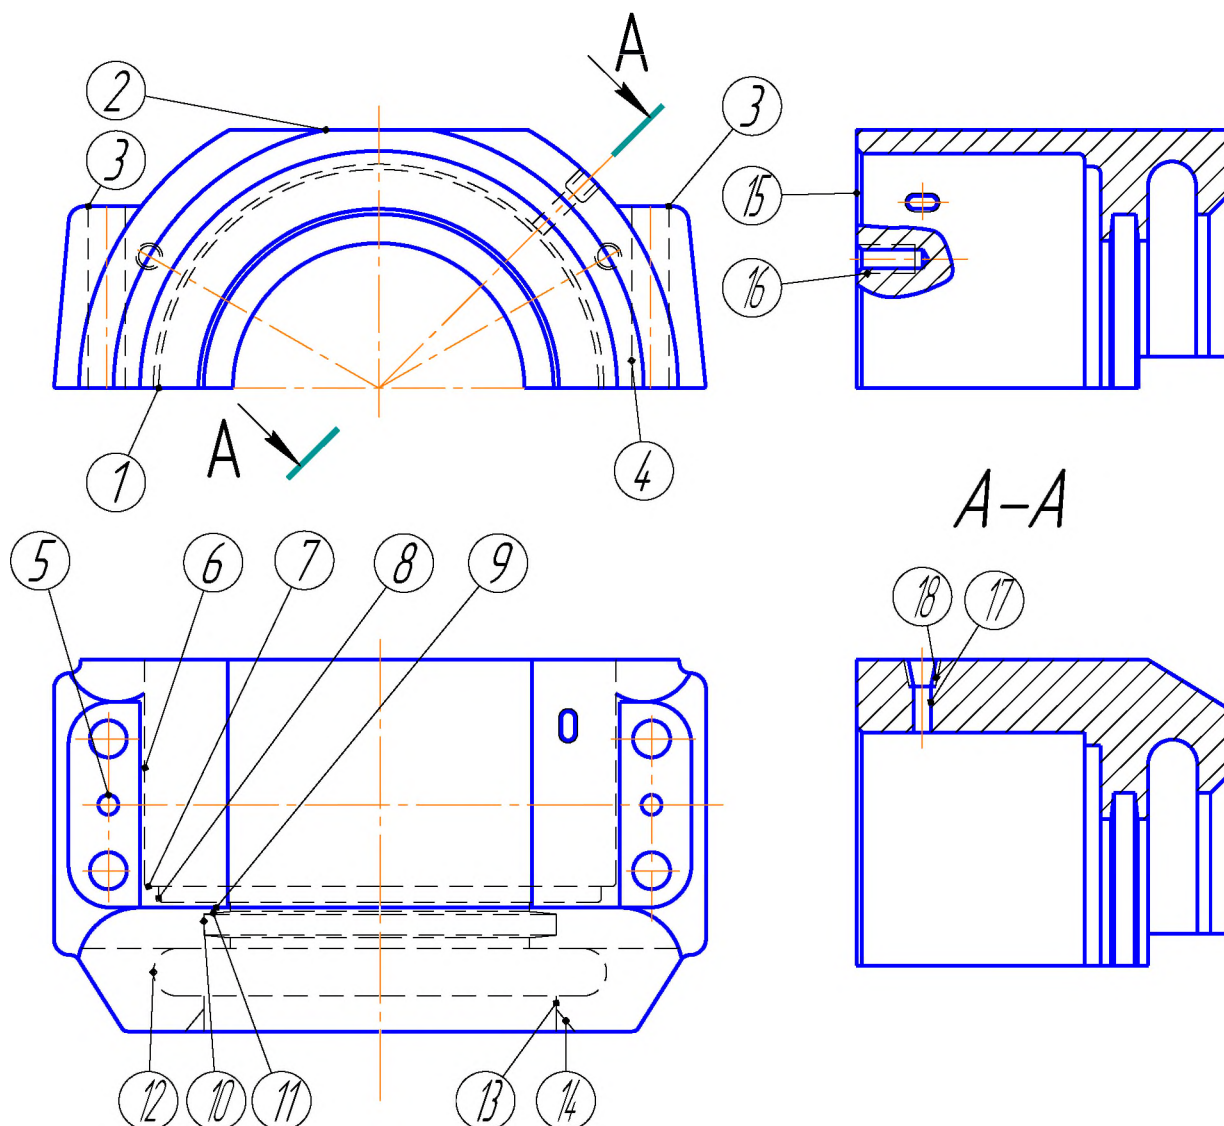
Схема деталі з пронумерованими поверхнями
